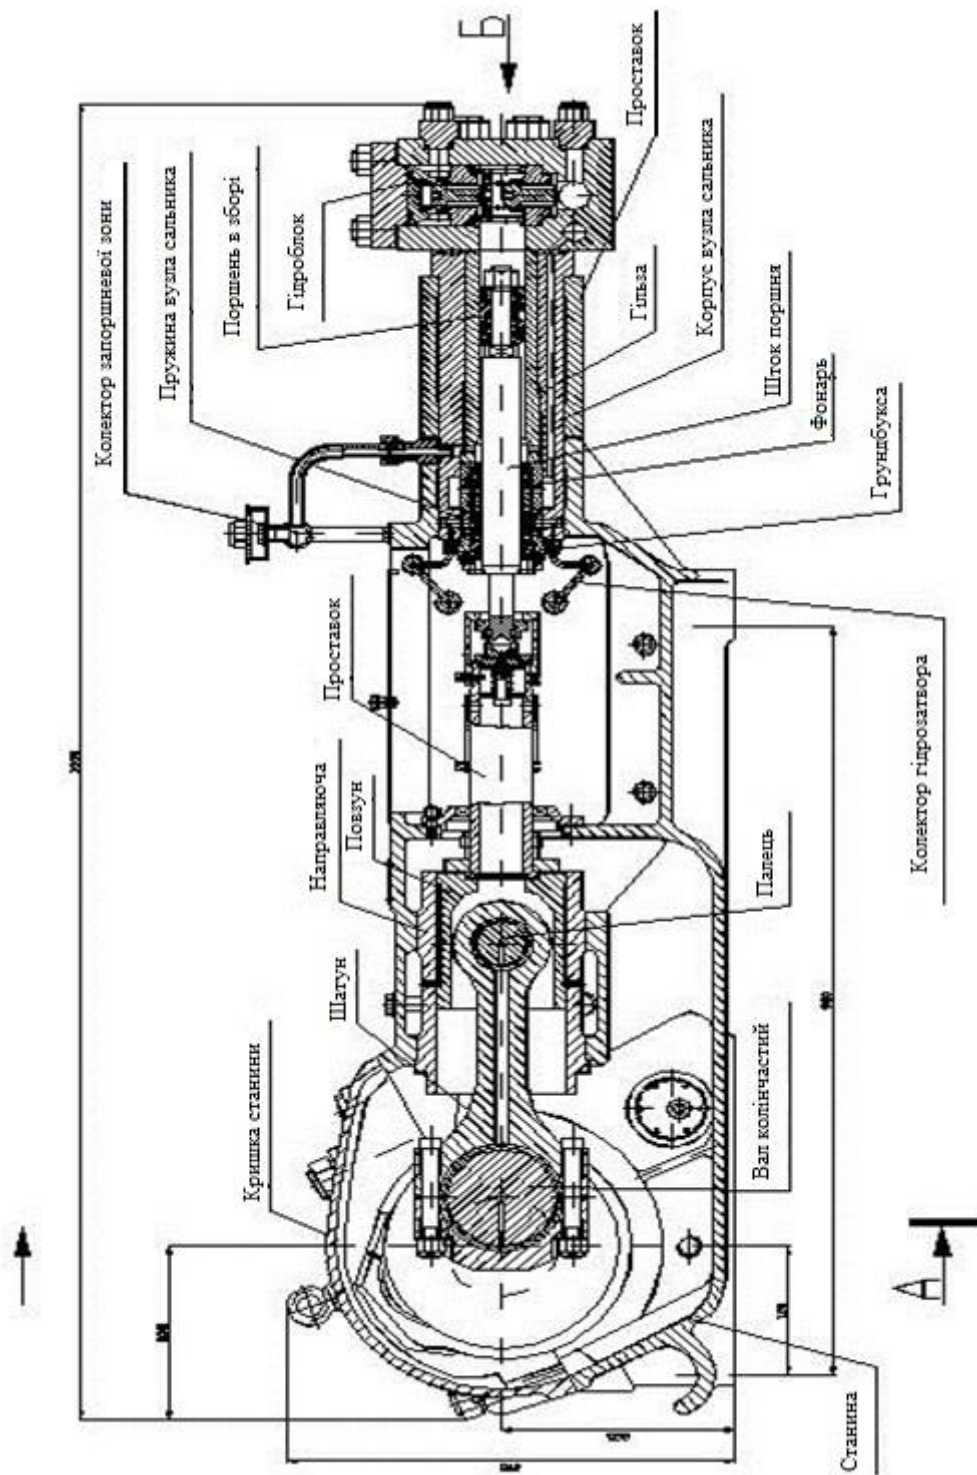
Креслення насоса ПТ6 / 160-С - поздовжній розріз [122]
